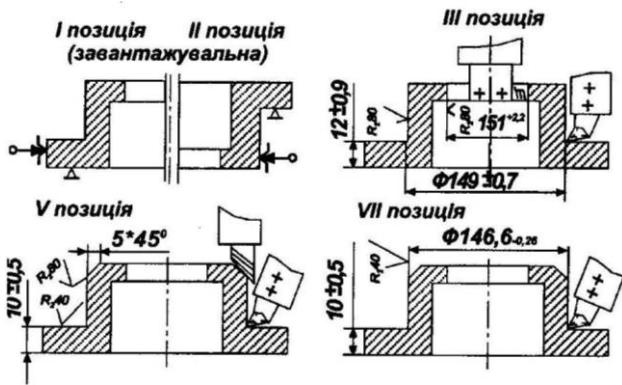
Схема наладки токарного восьмишпindelного напiвавтомата для двохциклової обробки стаканa роликoпiдшипника – обробка з установкою на I позицiї
